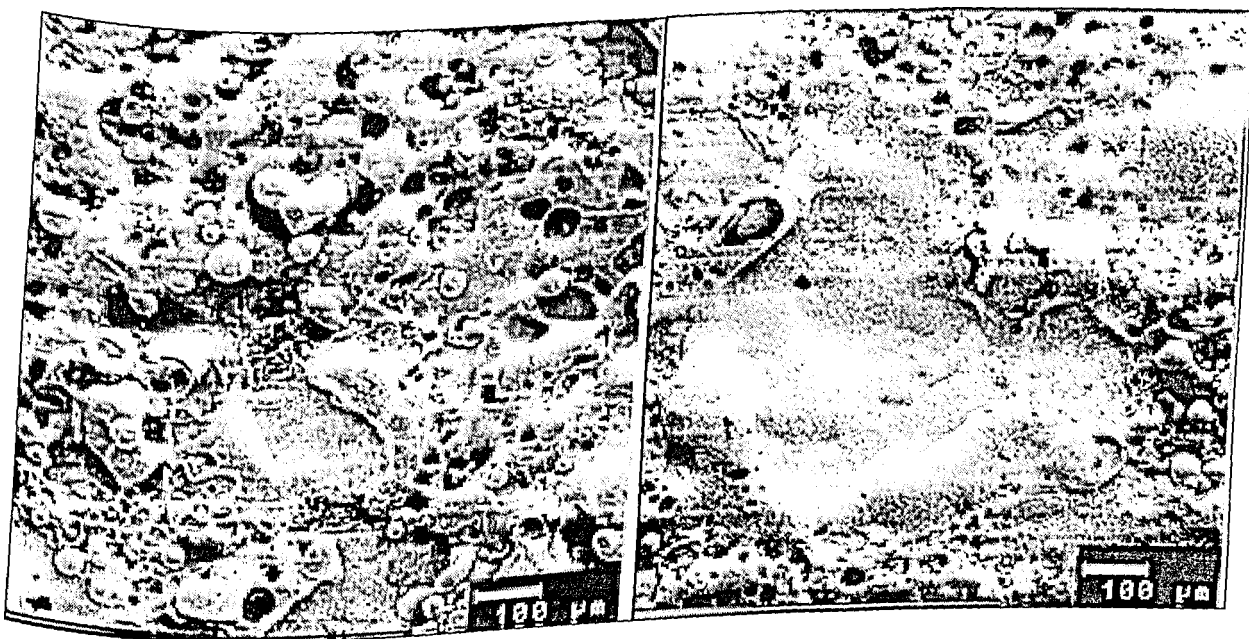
Vista superior das superfícies usinadas com o fluido dielétrico A, MEV.
